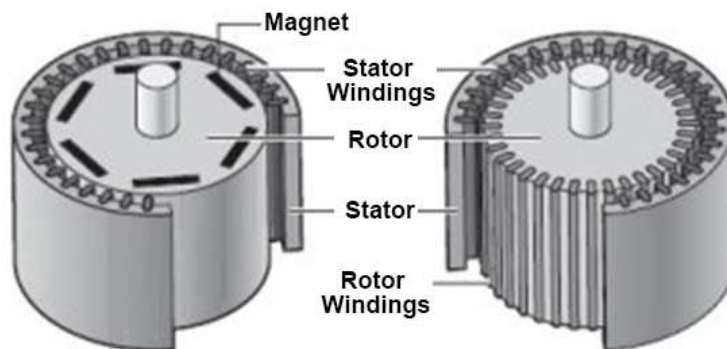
MSIP (izquierda), Motor de inducción (derecha)
